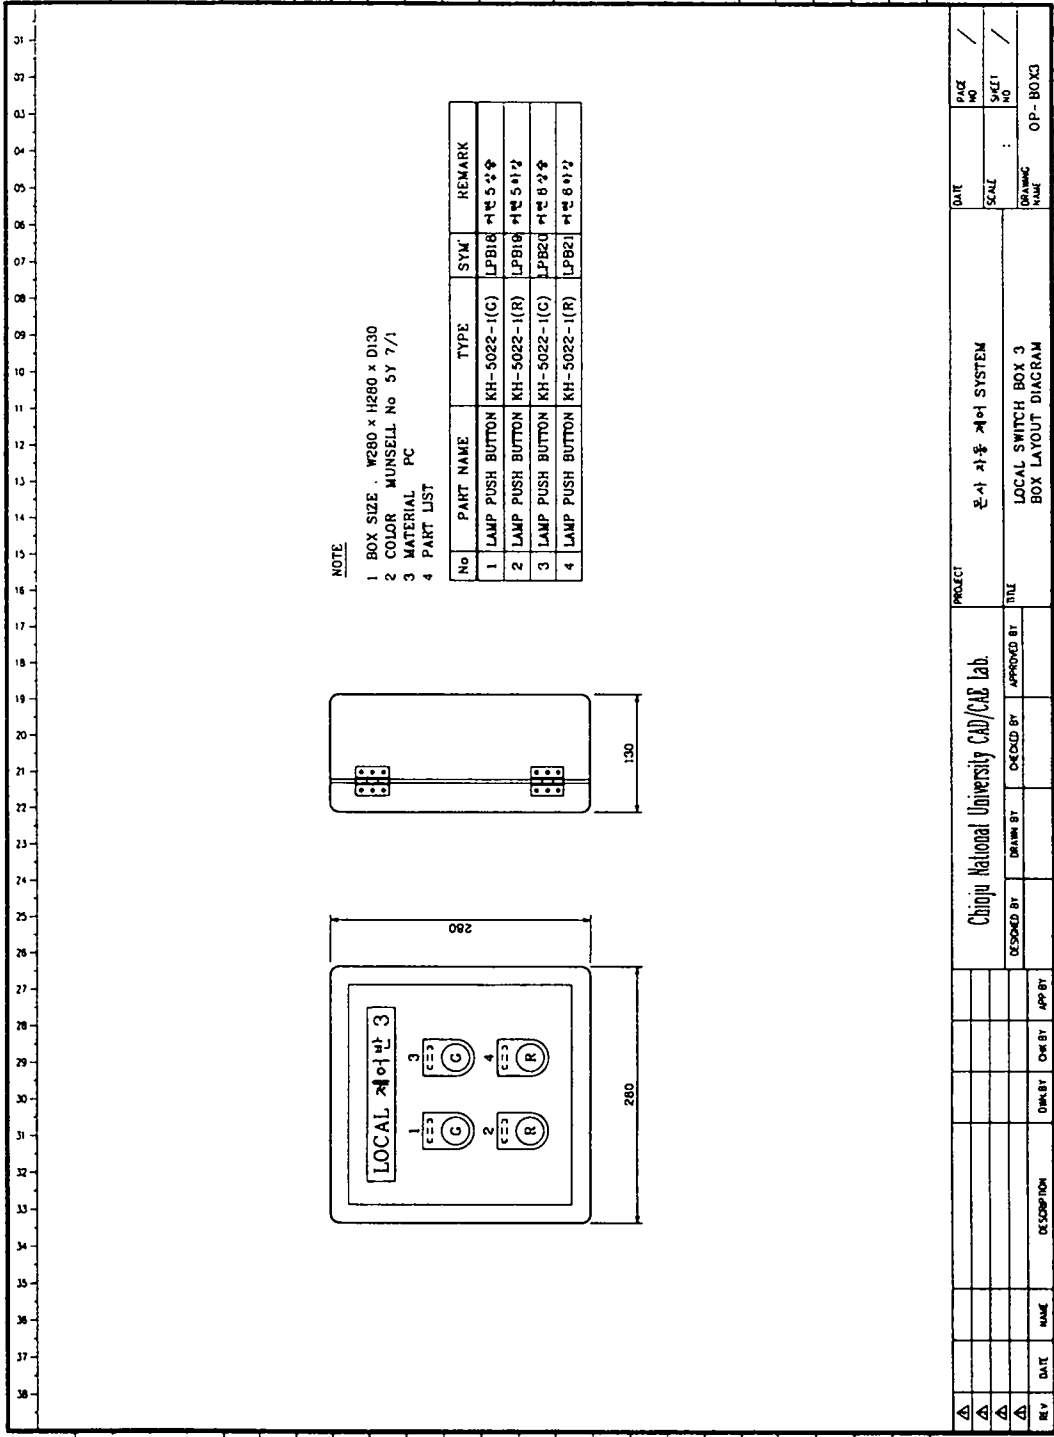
스위치 박스 배치도(Local switch box layout diagram) #3
